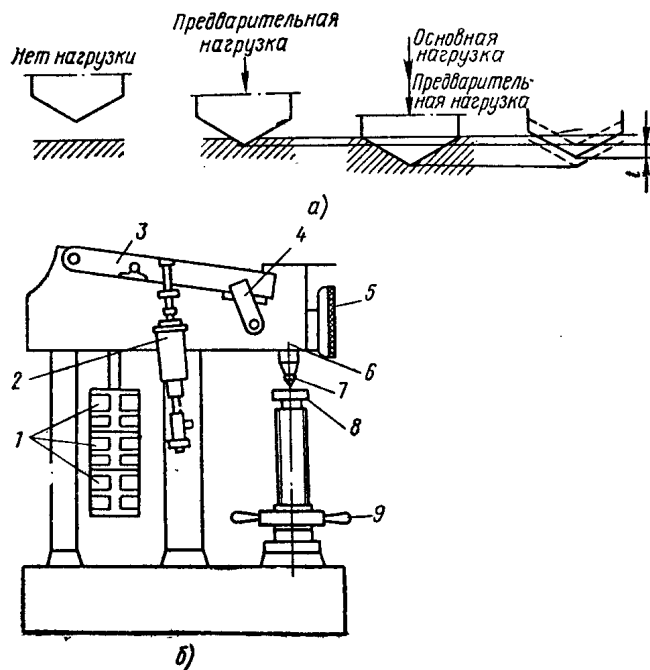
Определение твердости металла по Роквеллу: — ТК (твердомер конусный):
